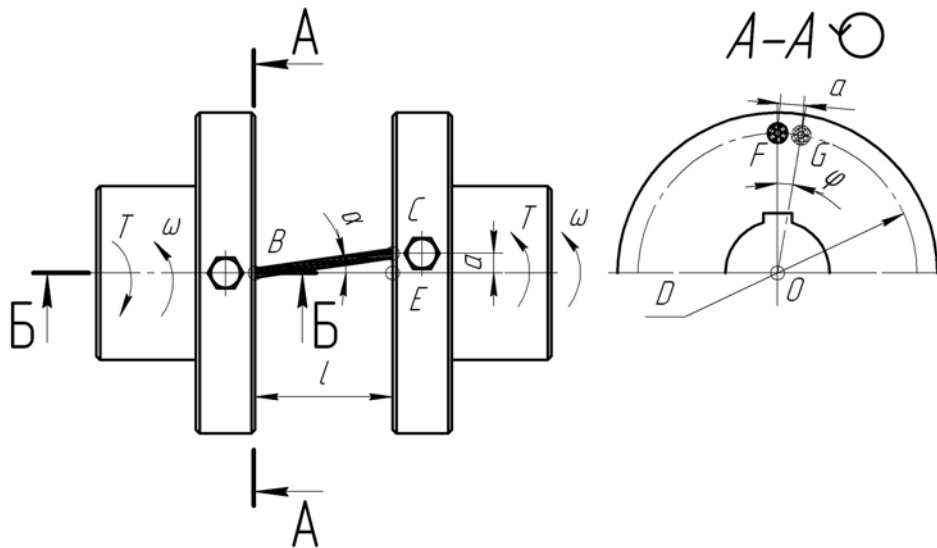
Схема муфти з осью паралельною установкою канатів прямолінійної форми
